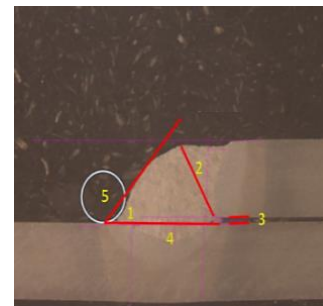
Zonas geométricas de interés de unión soldada
